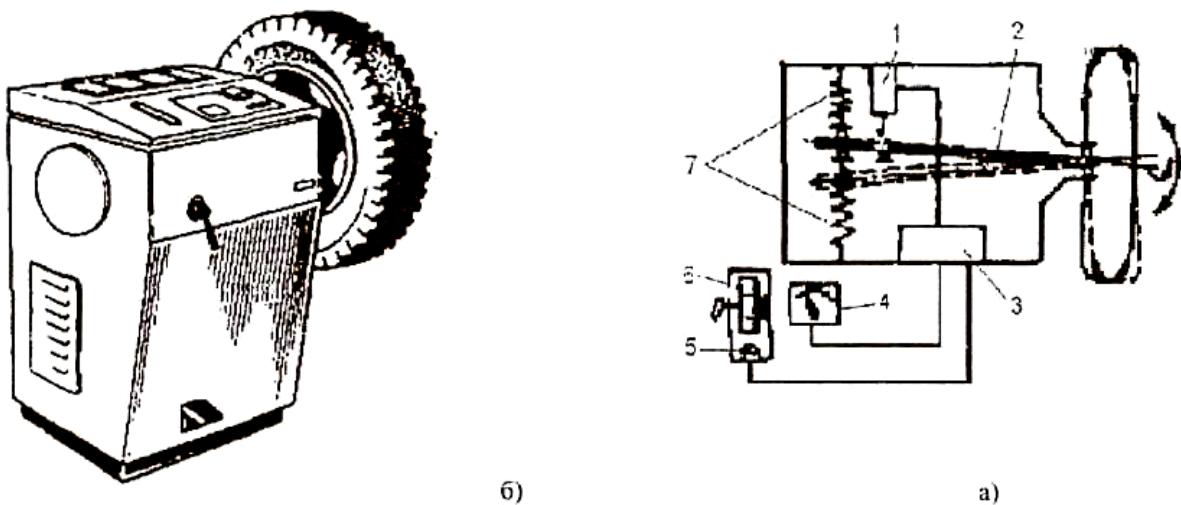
Станок для динамической балансировки колес легковых автомобилей: а - общий вид; б - схема
